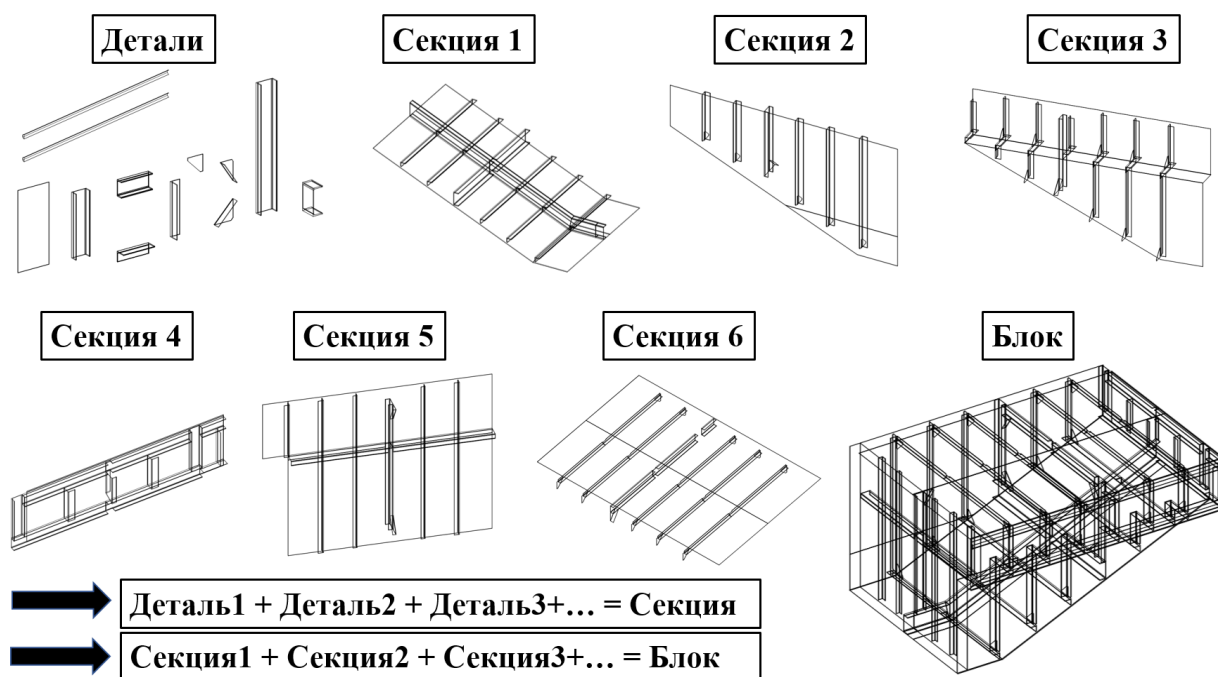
Изготовление и сборка секций и блока оконечности
